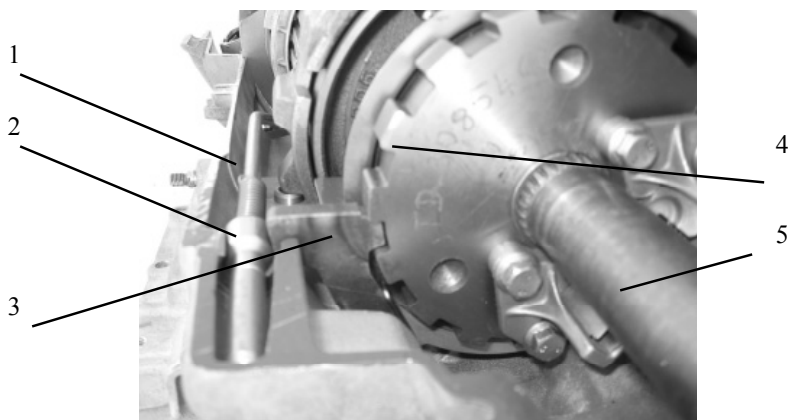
Механизм парковки. Положение «парковка включена»: 1 – тяга; 2 – блокировочный конус; 3 – блокировочный упор; 4 – блокировочная шестерня; 5 – ведомый вал
